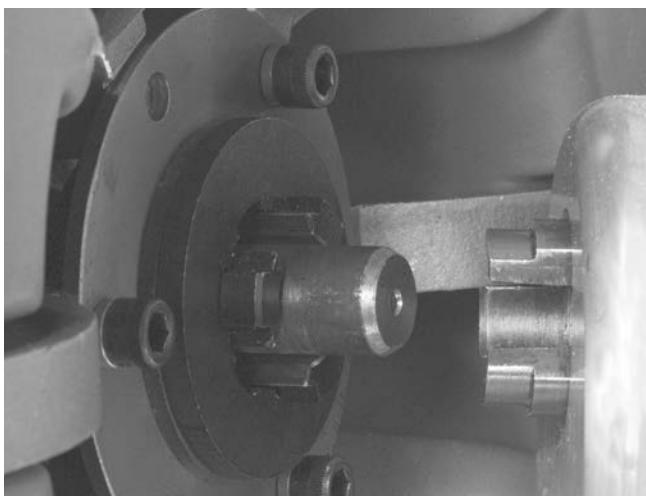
Instalación del conjunto del tambor hacia la caja de engranajes
